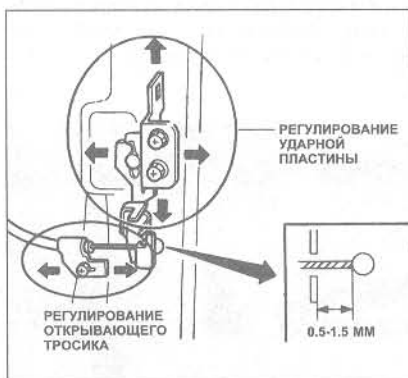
Регулирование ударной пластины крышки багажника и открывающего тросика - Седан (Глава 22)
